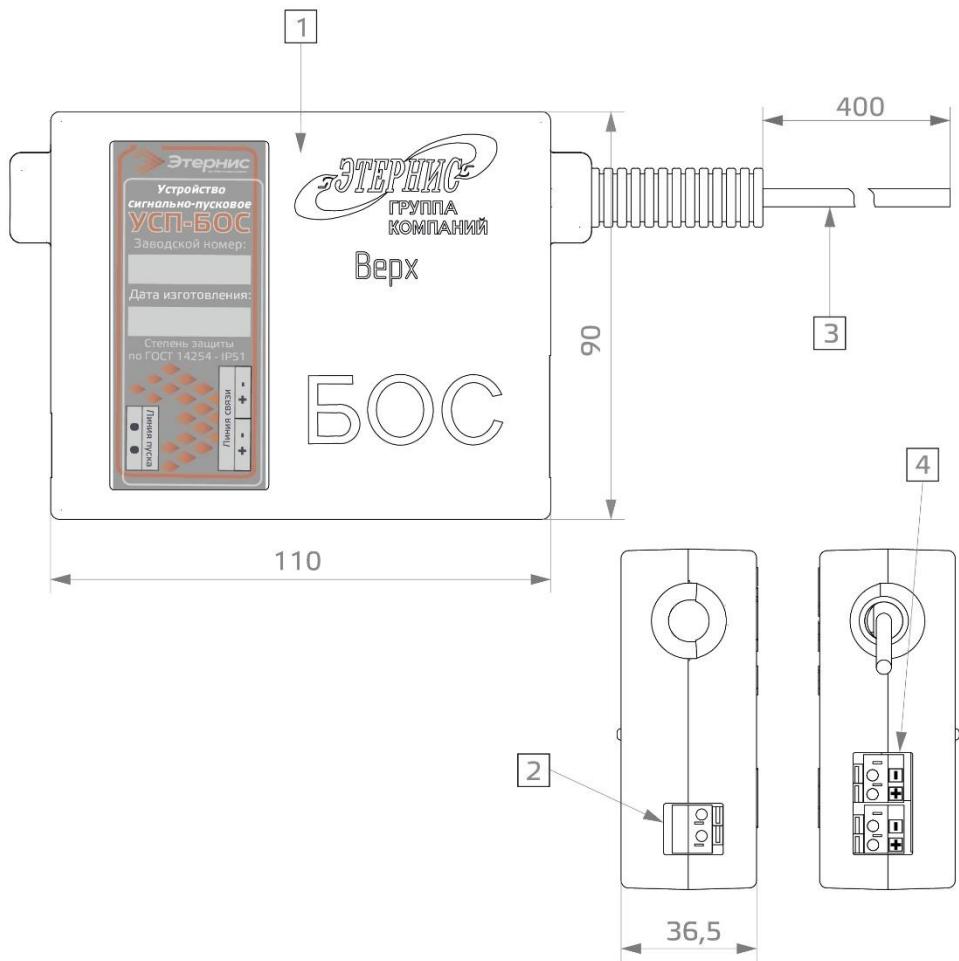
Внешний вид Устройства сигнально-пускового «УСП-БОС».
